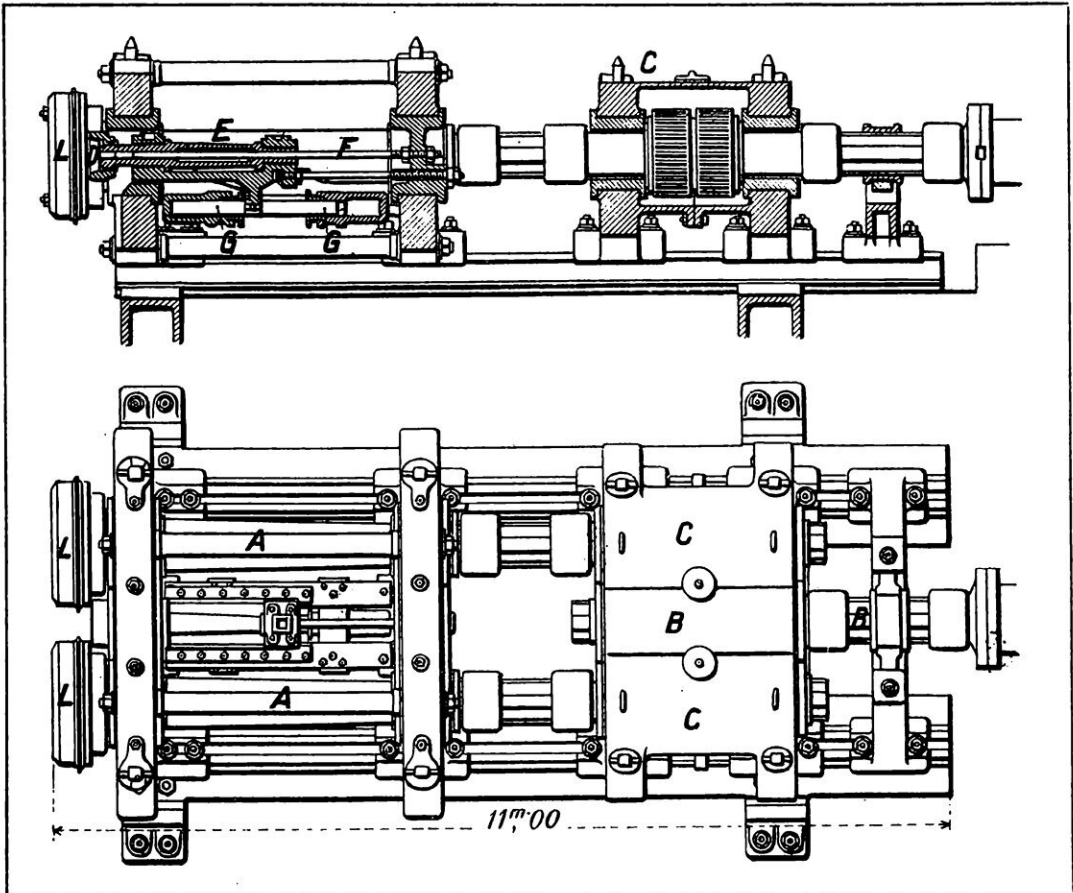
ÉLÉVATION ET PLAN DE LA CISAILLE SYSTÈME SLICK
